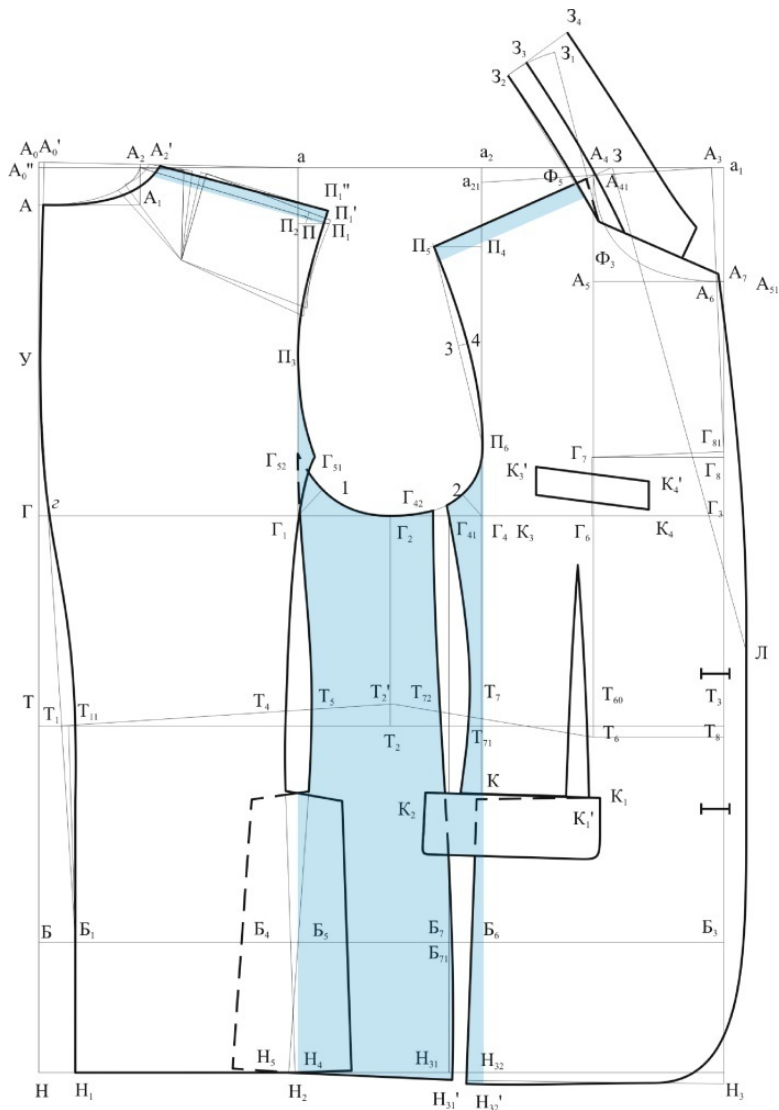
Чертеж модельной конструкции пиджака с обозначением «невидимой зоны» голубым цветом
